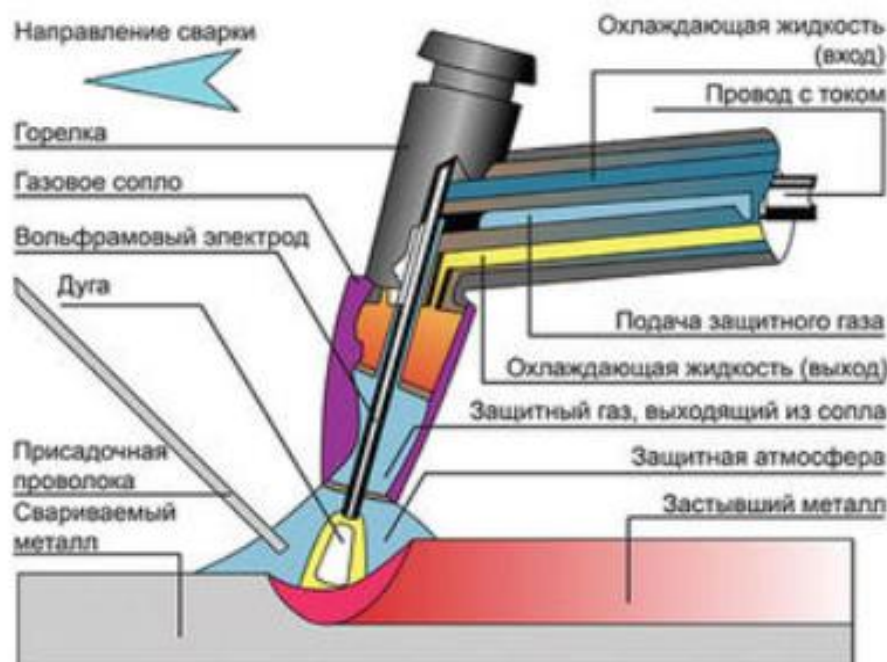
Механізований спосіб електродугового зварювання
